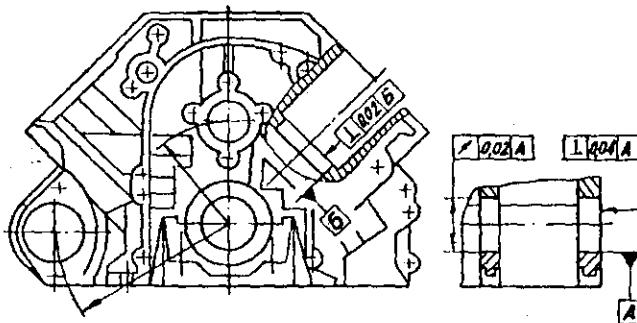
29. Блок цилиндров: А и Б – измерительные базы
